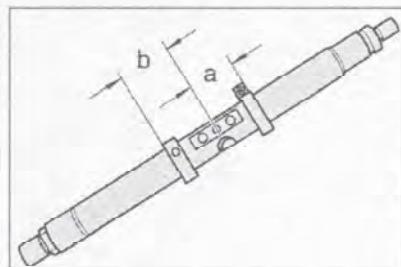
Отрегулируйте измерительное приспособление VW 385/1 на размер $a = 65 \text{ мм}$. Отрегулируйте установочное кольцо приспособления на размер $b = 65 \text{ мм}$.
